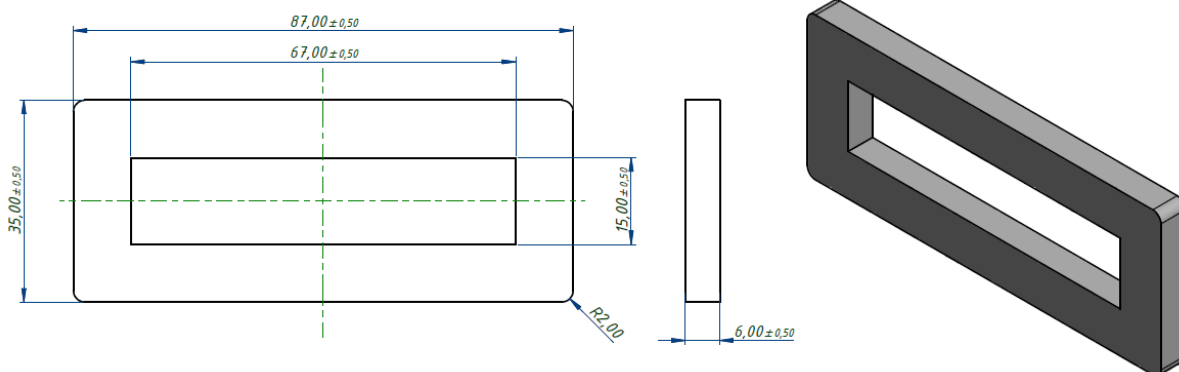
Molde para obtenção da amostra curada para usinagem dos corpos de provas.
